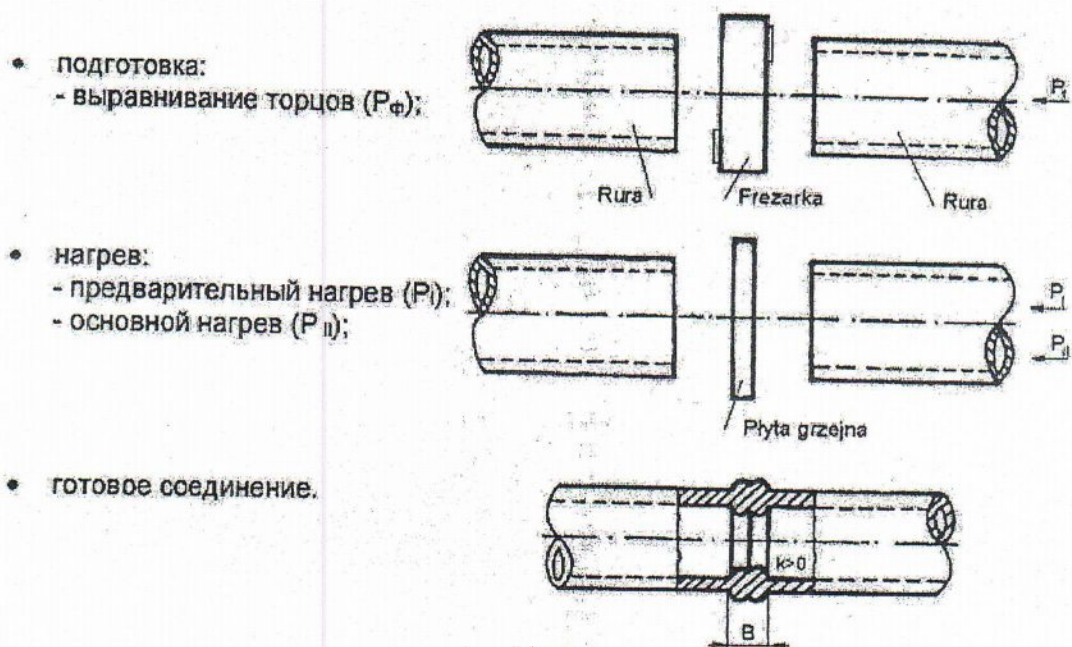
Этапы процесса стыковой сварки
